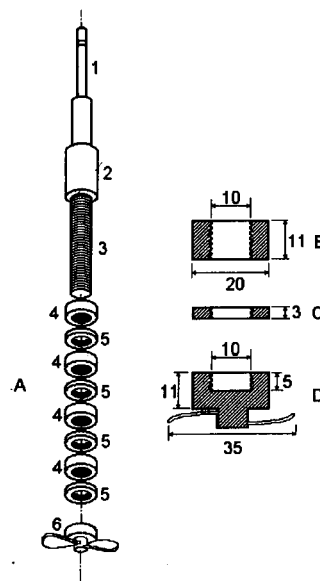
Detalhes do eletrodo rotatório. (A) - vista explodida do eletrodo: 1- eixo de aço inox, 2- isolante fixo, 3- rosca, 4- isolantes, 5- anéis de cobre, 6- hélice. (B) - Detalhe do isolante, (C) - Detalhe do anel, (D) - Detalhe da hélice.
